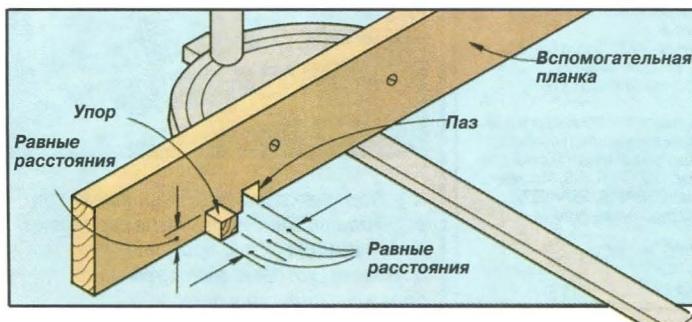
Приспособление для нарезания зубцов на циркулярке.
